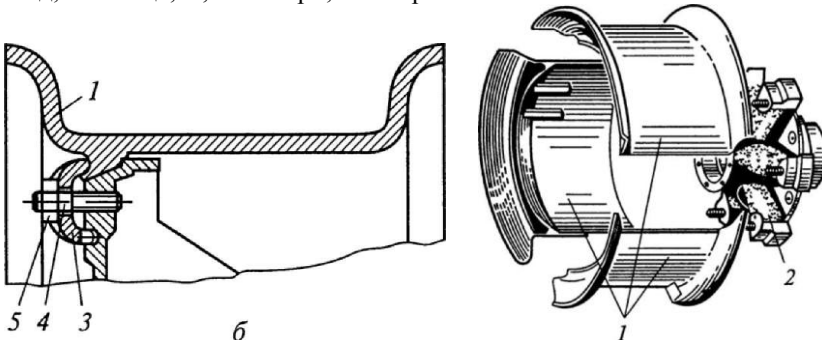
Елементи бездискового колеса: а - конструкція; б - кріплення; 1 - сектори обода; 2 - матчиною; 3 - притиск; 4 - шпилька; 5 – гайка.
